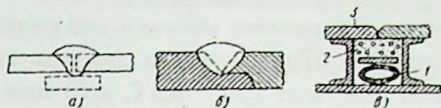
Схема автоматической сварки под флюсом:
